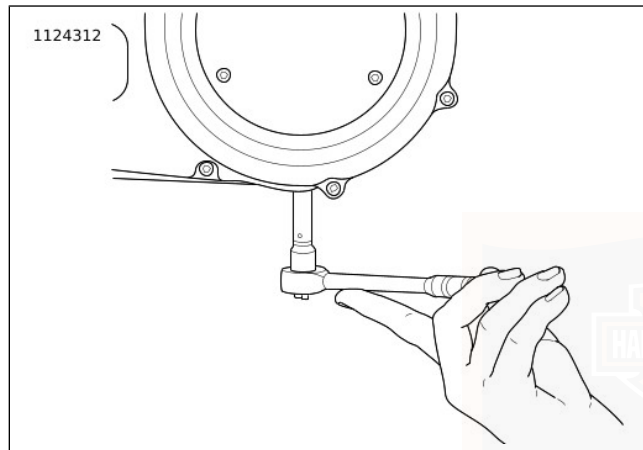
Extracción/instalación del tapón de drenaje del guardacadena
